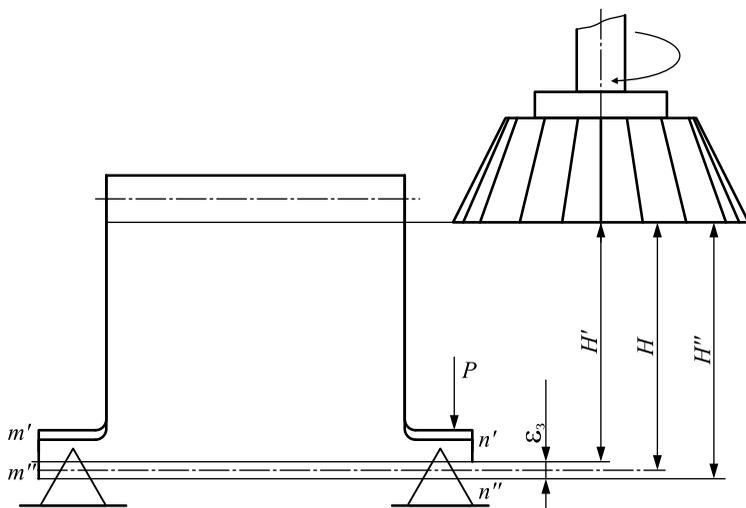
Схема осадки заготовки при закреплении с силой P , направленной перпендикулярно к опорной базе
